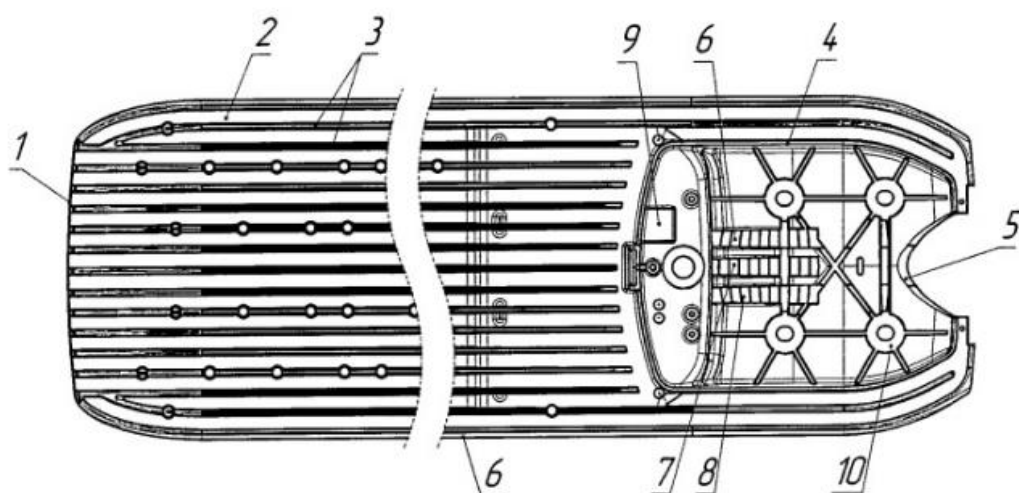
Чертеж общего вида светильника (вид сверху) [3]
